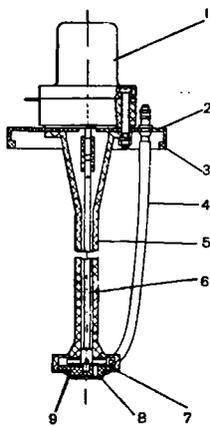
Насос омывателя ветрового стекла: 1 - электродвигатель; 2 - крышка питающего бачка; 3 - муфта; 4 - трубка подачи жидкости; 5 - корпус насоса; 6 - вал ротора; 7 - опора вала ротора; 8 - ободок с сеткой фильтра; 9 - ротор
